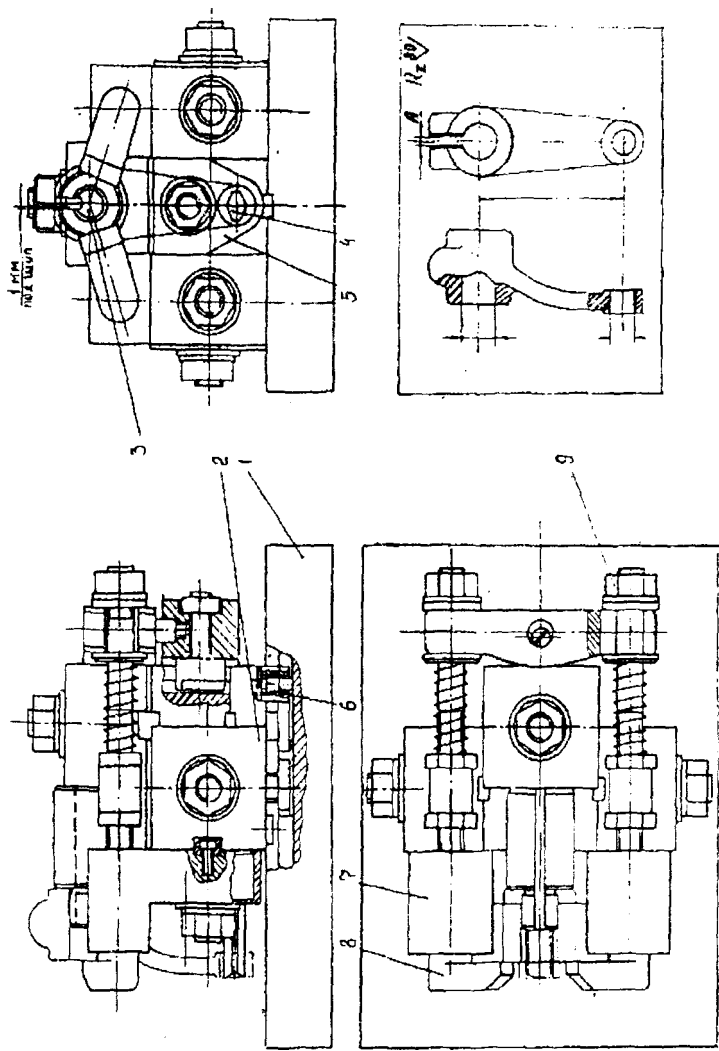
Универсально-сборное приспособление для фрезерования паза в заготовке
